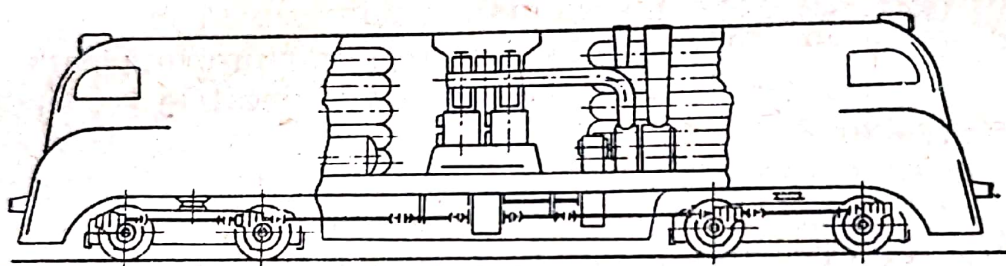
Locomotivă acționată prin generatoare de gaze cu pistoane libere. Combustibil-gaz metan; transmisie turbo-mecanică.
